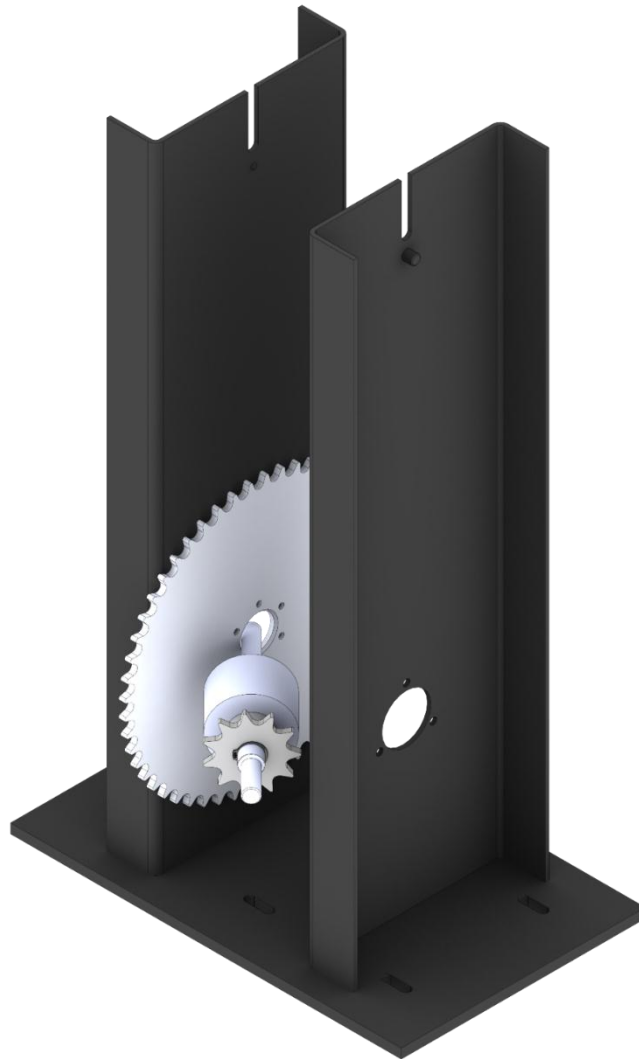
Muntatge de l'eix intermedi al subconjunt de soldadura de l'estructura motor.
